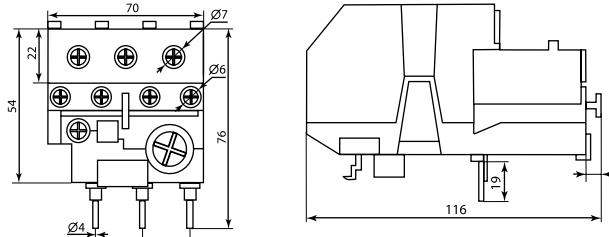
Габаритные и установочные размеры реле РТИ-3353...РТИ-3366
